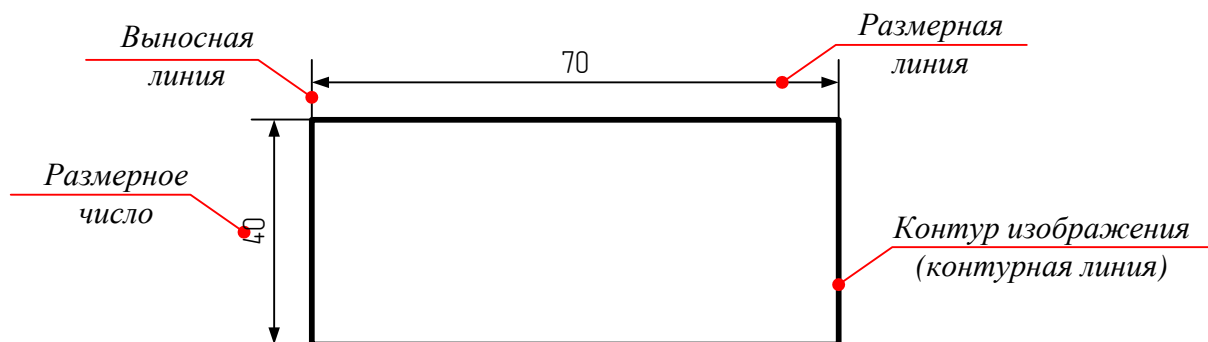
Выносные и размерные линии с размерным числом на чертежах
